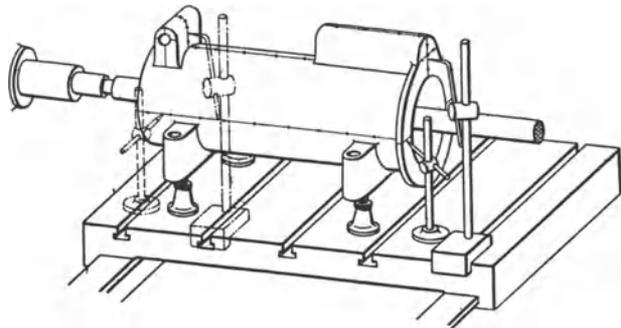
Ausrichten eines Werkstückes nach zwei Mittelrissen auf dem Bohrwerk.
